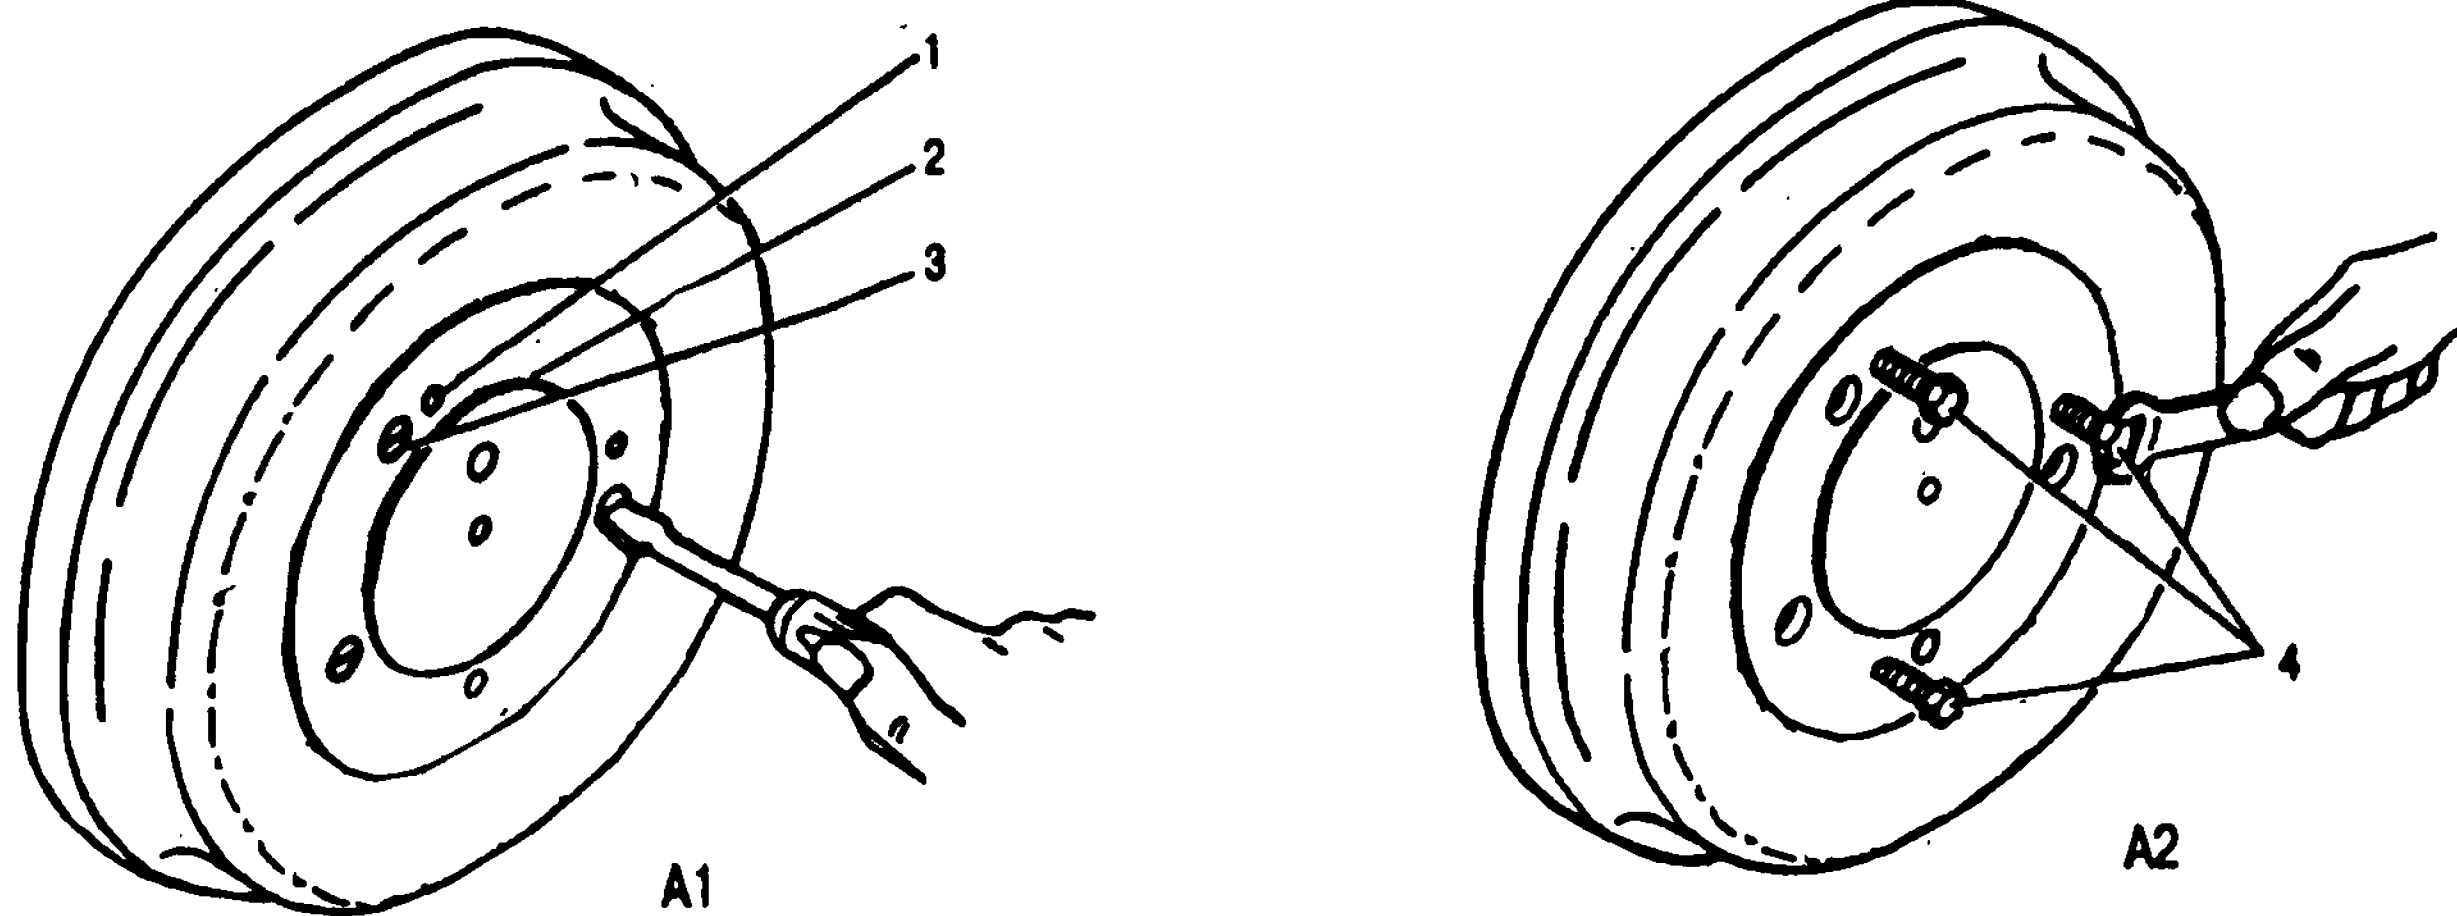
Снятие тормозного барабана: 1 - отверстия для съемных болтов, 2 - болты крепления колес; 3 - винты крепления тормозного барабана; 4 - болты-съемники
